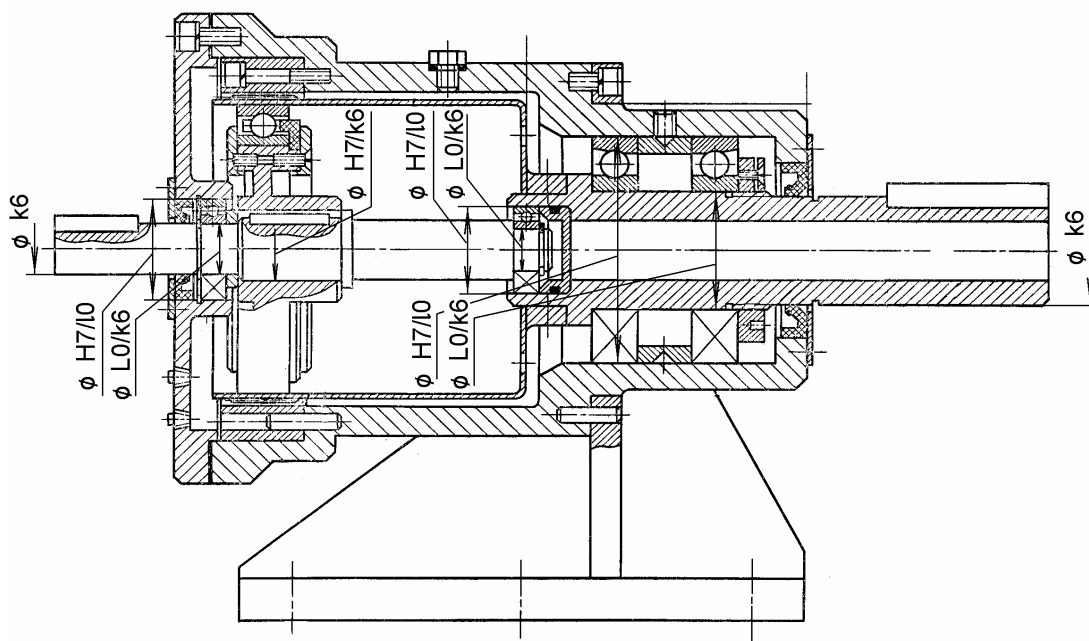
Волновой одноступенчатый зубчатый редуктор
